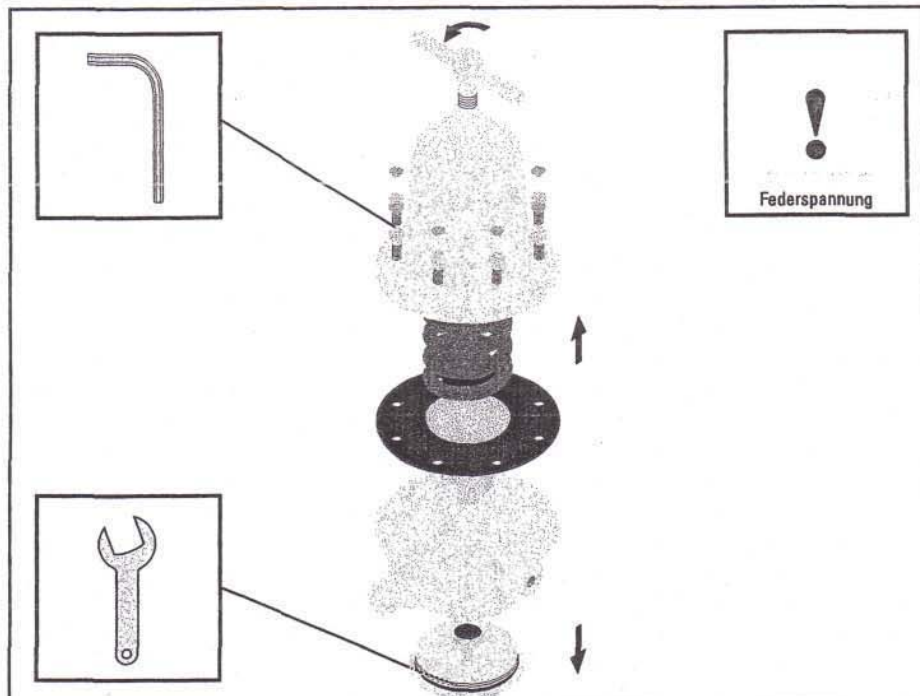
Druckminderer, Montage Anschweißenden, Zerlegen des Druckminderers (Abbildung zeigt Art. DM330362).
